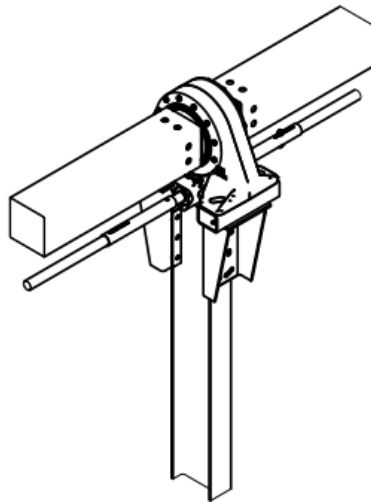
Profilato a sezione quadrata longitudinale alle strutture su cui avviene il movimento dei tracker
